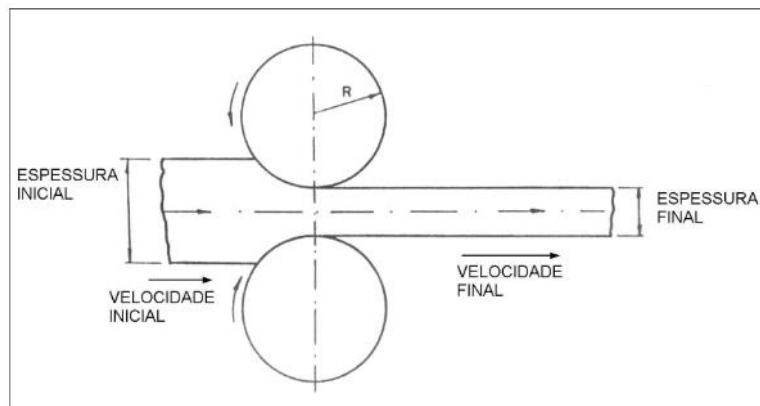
Esquema do movimento do material durante a Laminagem [3].
